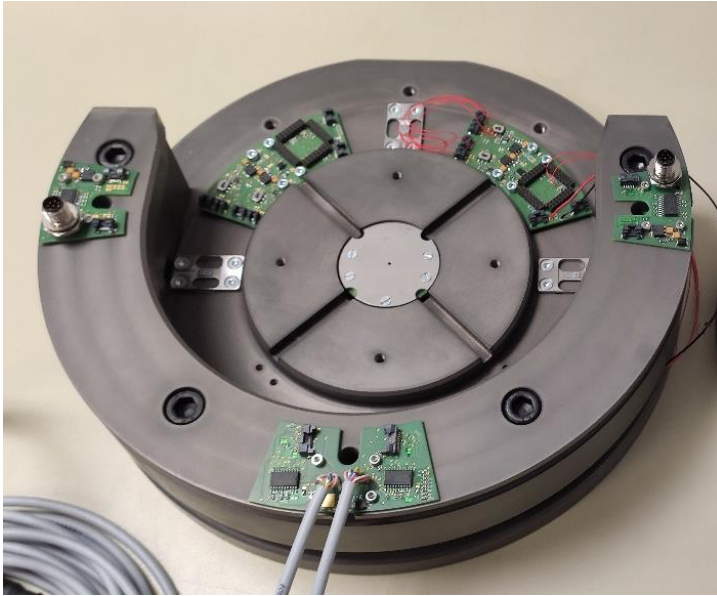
HYDAC-Sensorwerkzeug mit Kraftsensor-Platinen
